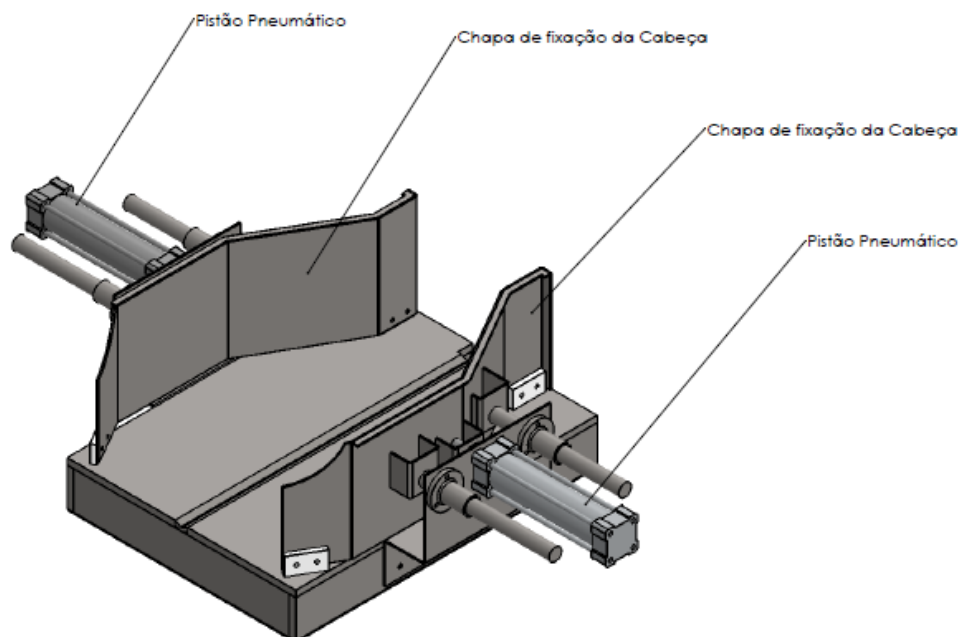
Pistão Pneumático e Chapa de fixação de Cabeça.
